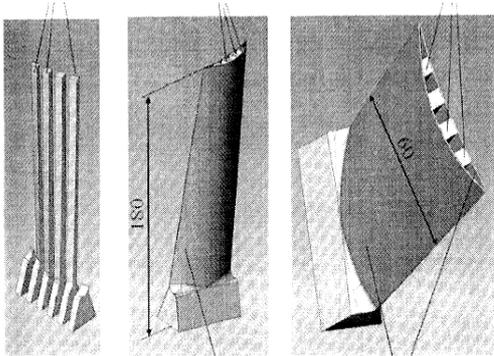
Широкохордная полая лопатка с несущими элементами из боралюминия
